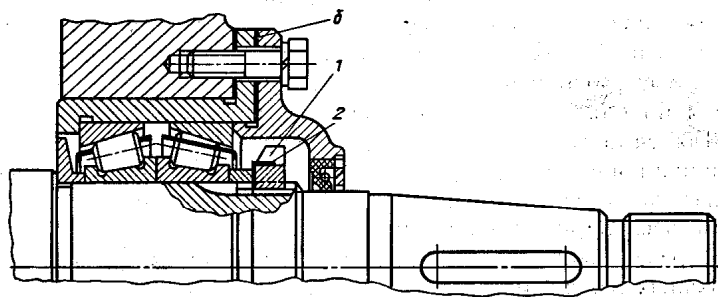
Способ крепления опоры вала (конические подшипники поставлены враспор)
